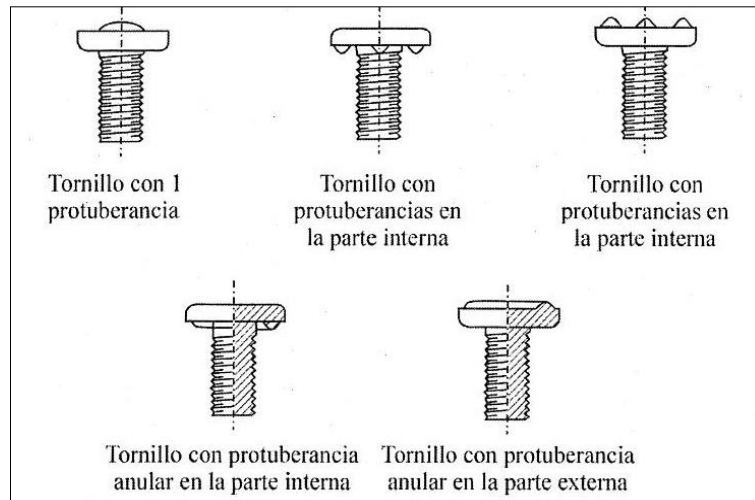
Diferentes tipos de tornillos aptos para ser soldados por proyección.
